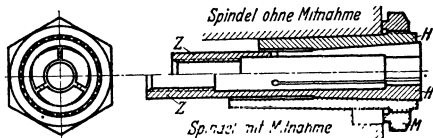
Einspannen von Fräsern mit zylindrischem Schaft.
